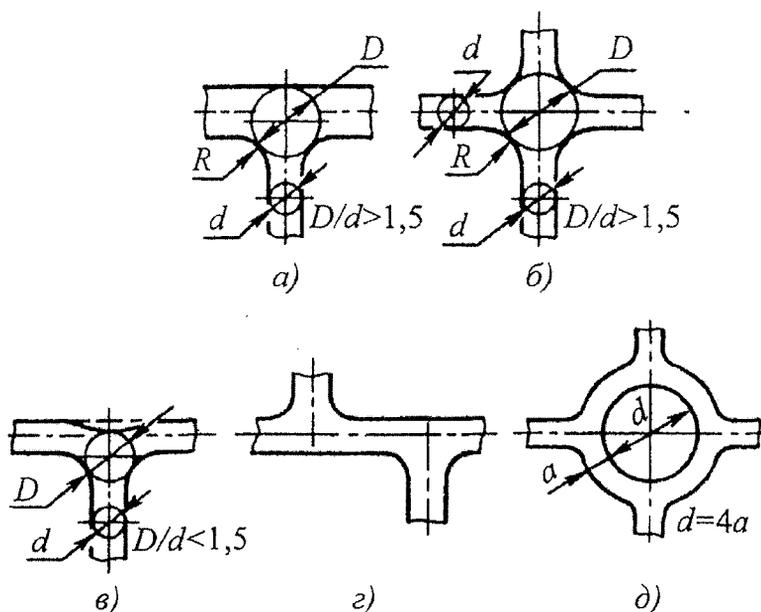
Устранение местного скопления металла в стенках отливки
